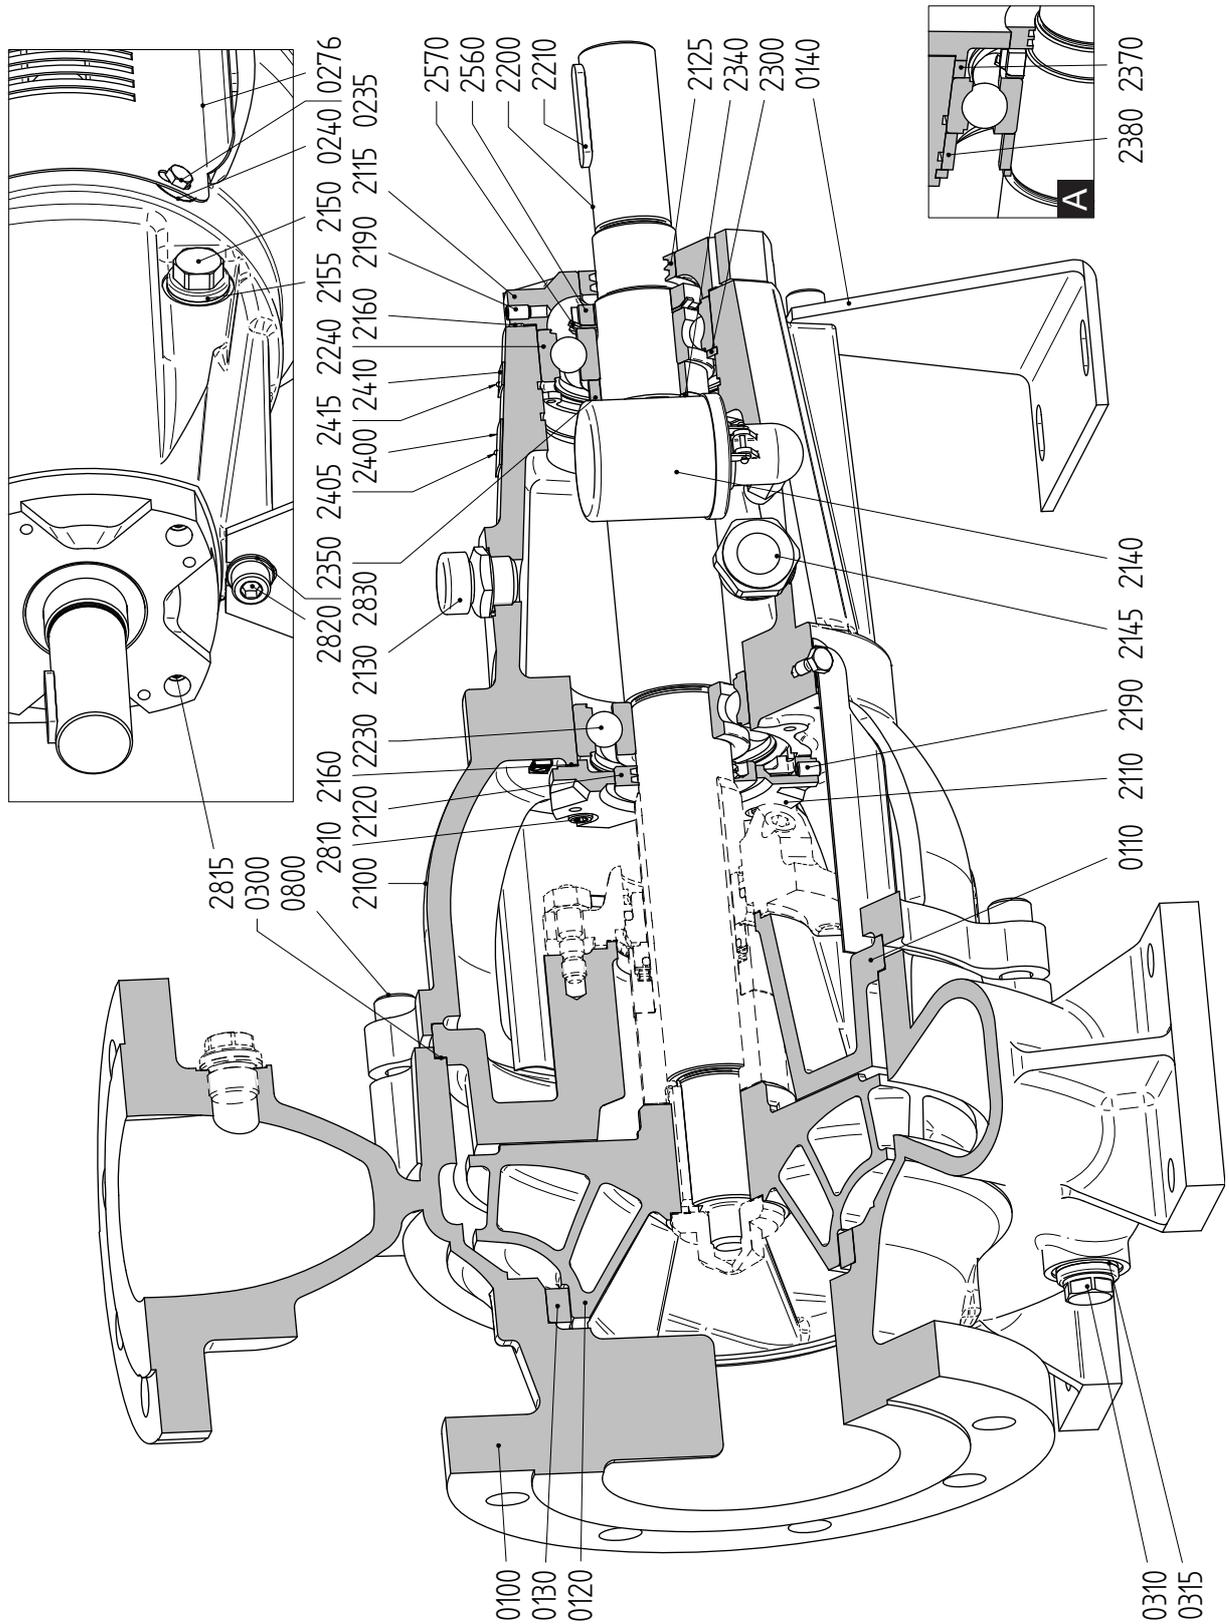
Schnittzeichnung L3 mit konischer Bohrung (A = für Lagergruppe 3).
